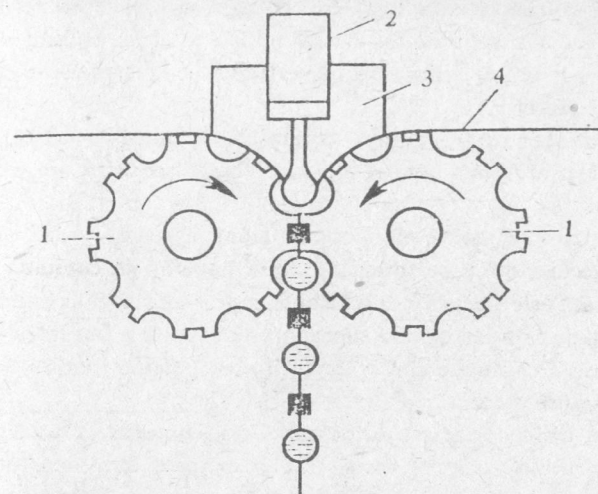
Schema funcționării unei mașini cu multe matrițe rotative pentru fabricarea capsulelor gelatinoase: 1 - tambur rotativ; 2 - dispozitiv cu piston; 3 - dispozitiv cuneiform; 4 - bandă de gelatină
